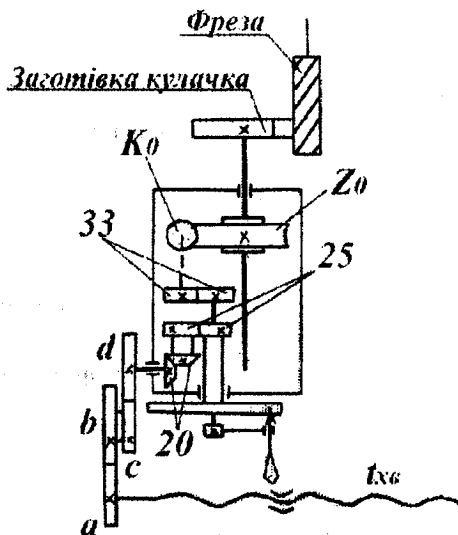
Кінематична схема для фрезерування поверхні кулачка по спіралі Архімеда
